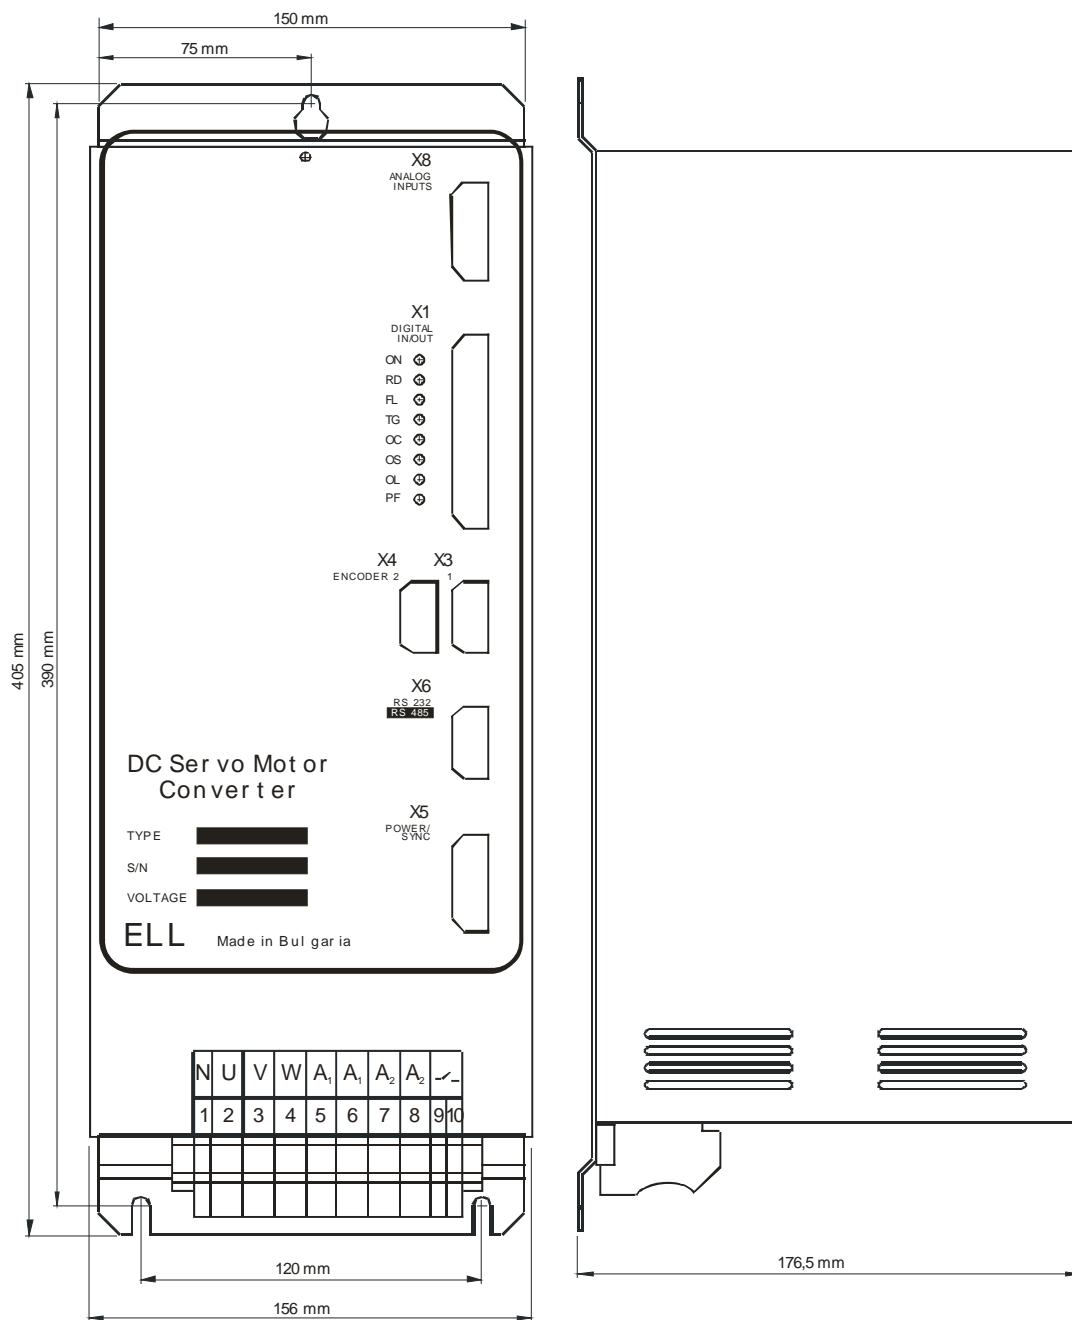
Присоединительные и габаритные размеры преобразователя типа 14080
